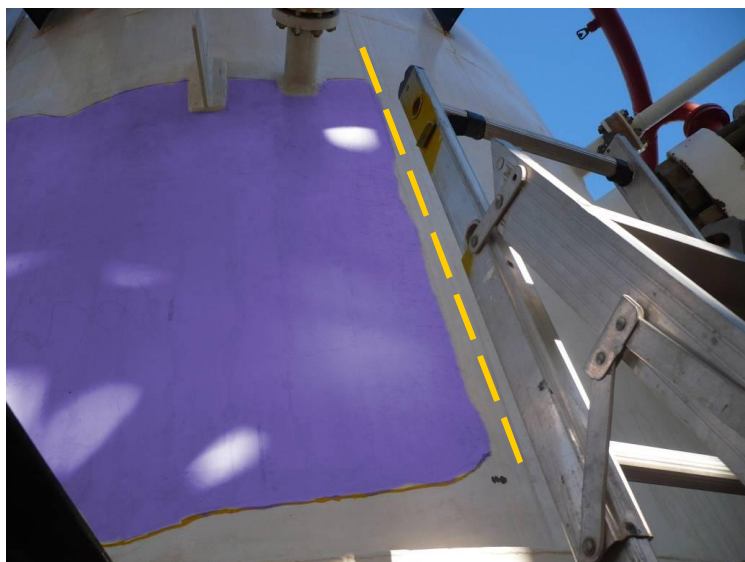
Niple, soporte y soldadura en zona laminada
